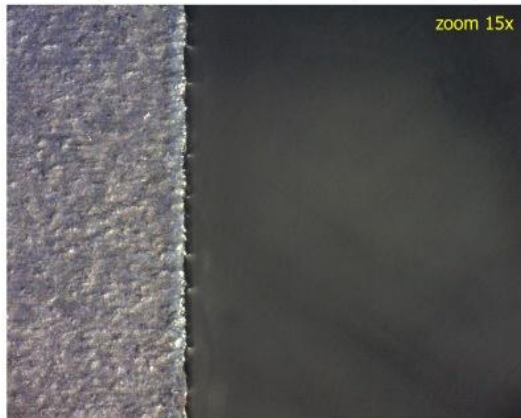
Snímky z mikroskopu vzorku 1 obráběného laserem - materiál 11 375
